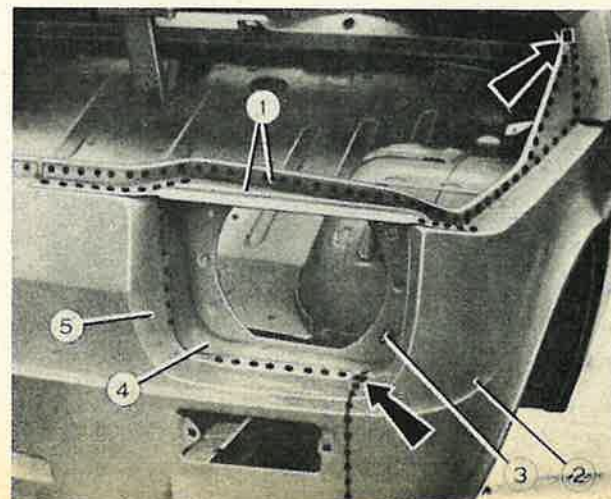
Liaisons par points de soudure des pièces composant le passage de roue avant droit.
